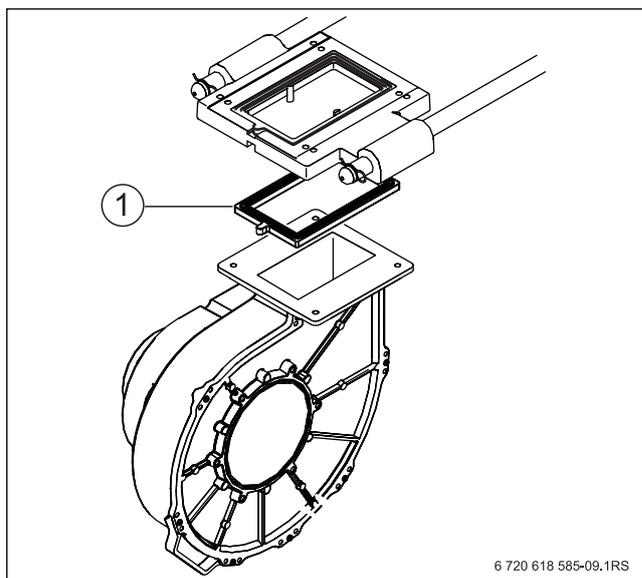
Remplacer le joint du ventilateur/support-glissoir
